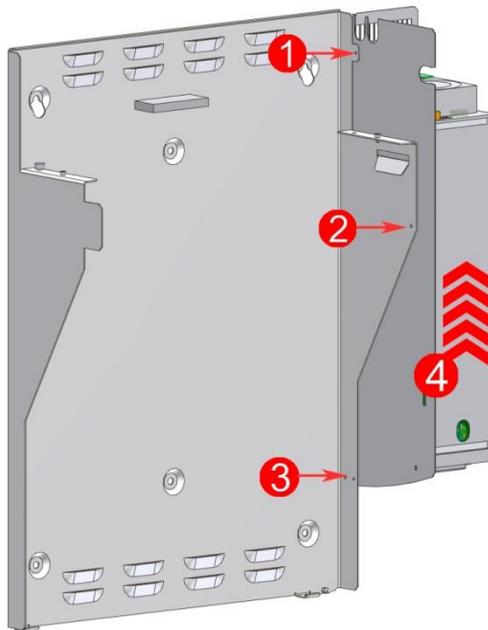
Schrauben am Batteriewechselrichter lösen
